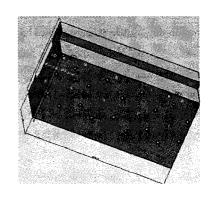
被加工零件及其 PMI 信息表示 Fig. 3 Machined parts said its PMI information
